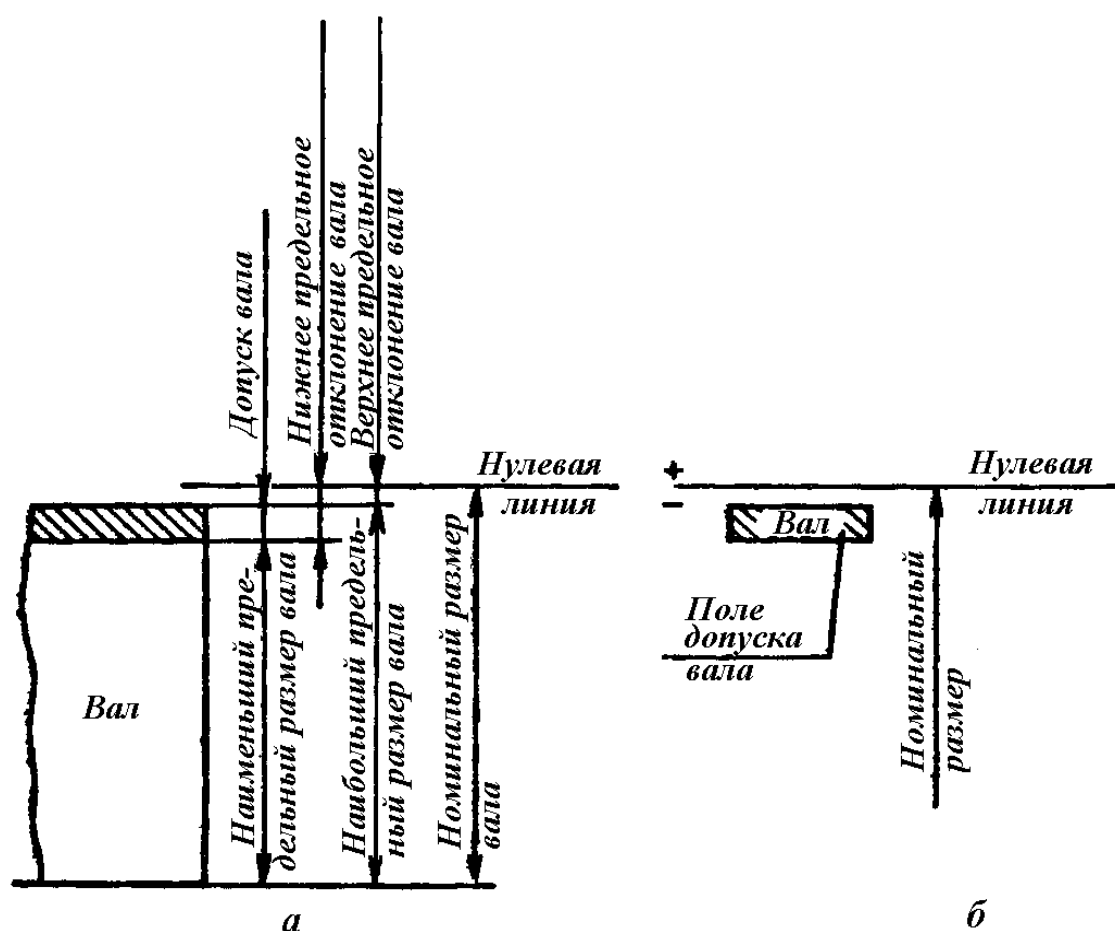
Графическое изображение размеров, отклонений и поля допуска вала: а – с указанием предельных размеров; б – с указанием поля допуска
